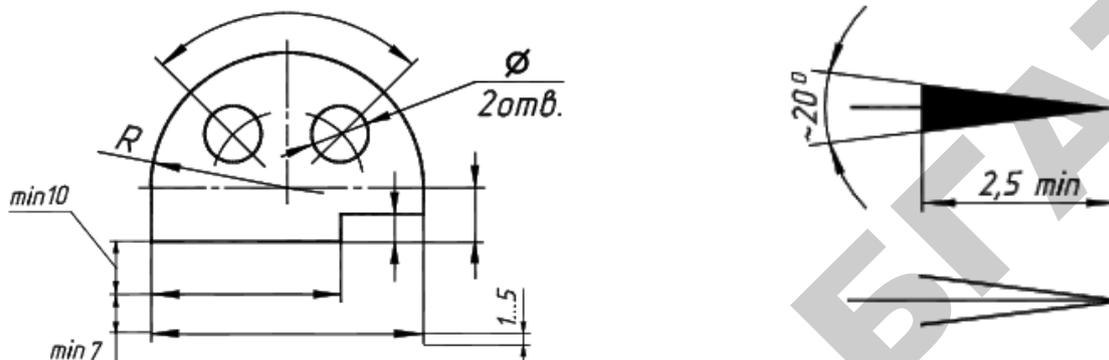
Примеры нанесения размерных линий и стрелок
